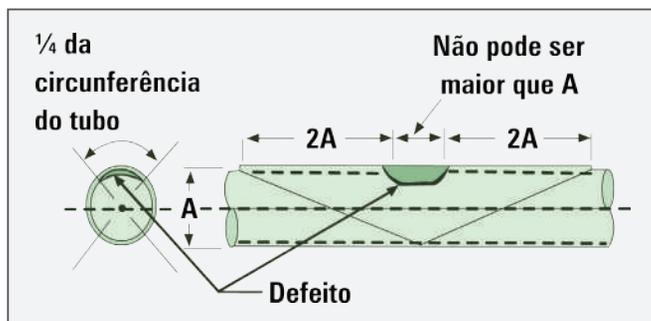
Dimensões do reparo por remendo soldado
